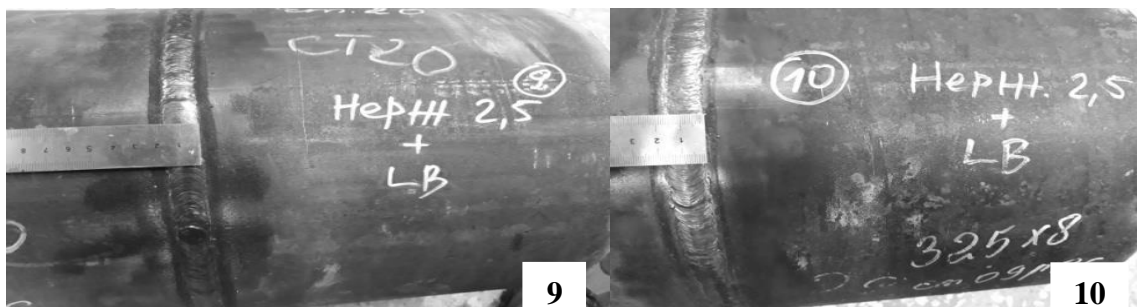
Сварное соединение 9. Рисунок Б20. Сварное соединение 10.
